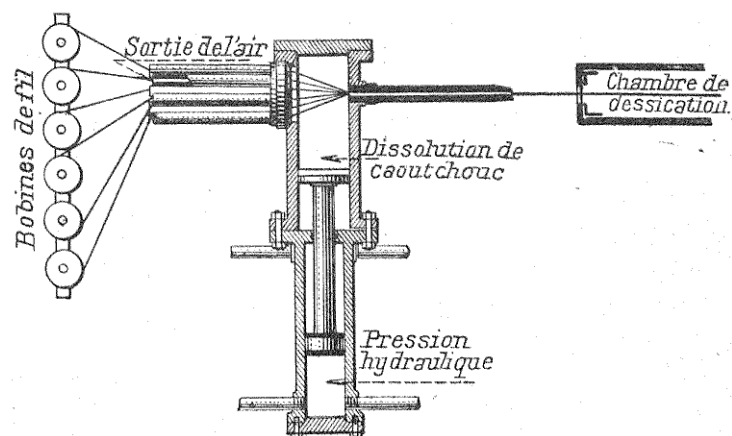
Machine à confectionner la corde privée d'air du pneu Palmer.
